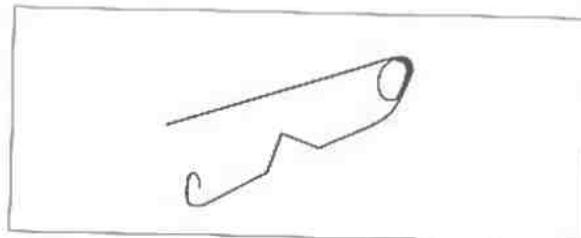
Схема изгиба булавки при изготовлении застежки броши
